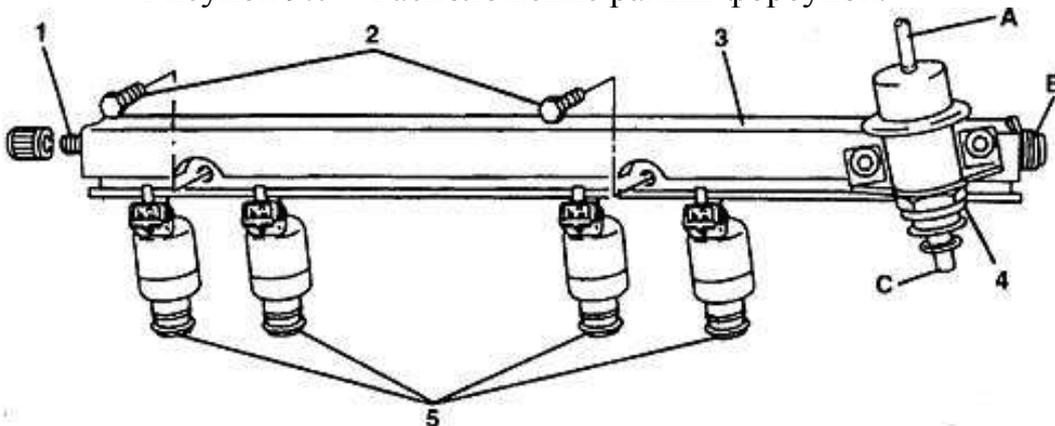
Рампа форсунок в сборе: 1- штуцер для контура давления топлива; 2- боты крепления рампы; 3 – рампа форсунок; 4 – регулятор давления топлива; 5- форсунки; А –патрубок отбора разряжения из впускной трубы; В – штуцер для подвода топлива; С- штуцер для слива топлива.
